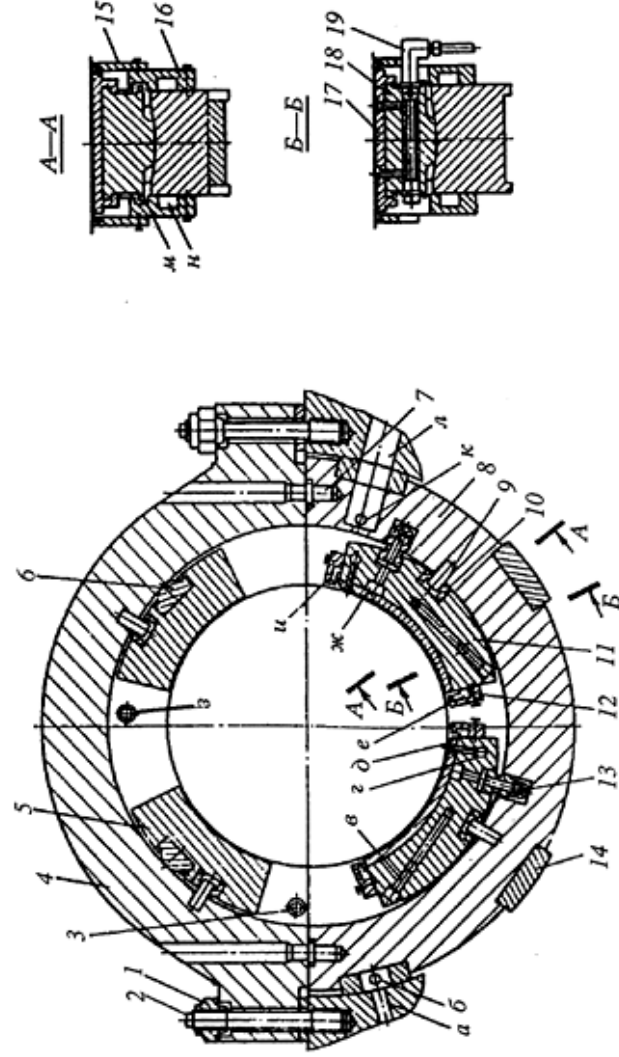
Сегментный подшипник конструкции ХТЗ: 1 – гайка; 2 – шпилька; 3 – сошло; 4 – крышка (бутиль) подшипника; 5 – сегмент верхний; 6 – упор; 7 – штифт; 8 – установочное полукольцо; 9 – штифт; 10 – втулка; 11 – сегмент нижний; 12 – накладка; 13 – шарнирная втулка; 14 – регулирующая колодка; 15 – уплотнения; 16 – крышка торцевая; 17 – накладка; 18 – опора (тело) сегмента; 19 – обратный клапан гидроподъема; а, б – каналы аварийного маслоподвода подшипника; в, г – маслоканалы гидроподъема; д – опорная накладка сегмента; е, и – накладки, образующие камеру подвода масла на смазку; ж – канал маслоподвода смазки к нижним сегментам; з – коллектор маслоподвода смазки к верхним сегментам; к, л – каналы основного маслоподвода подшипника; м – паз, удерживающий сегмент от выпадания; н – канал разводки масла смазки к сегментам
